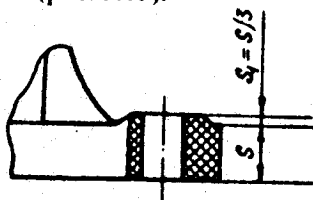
Опорна поверхня пластмасової деталі у вигляді бобишки
